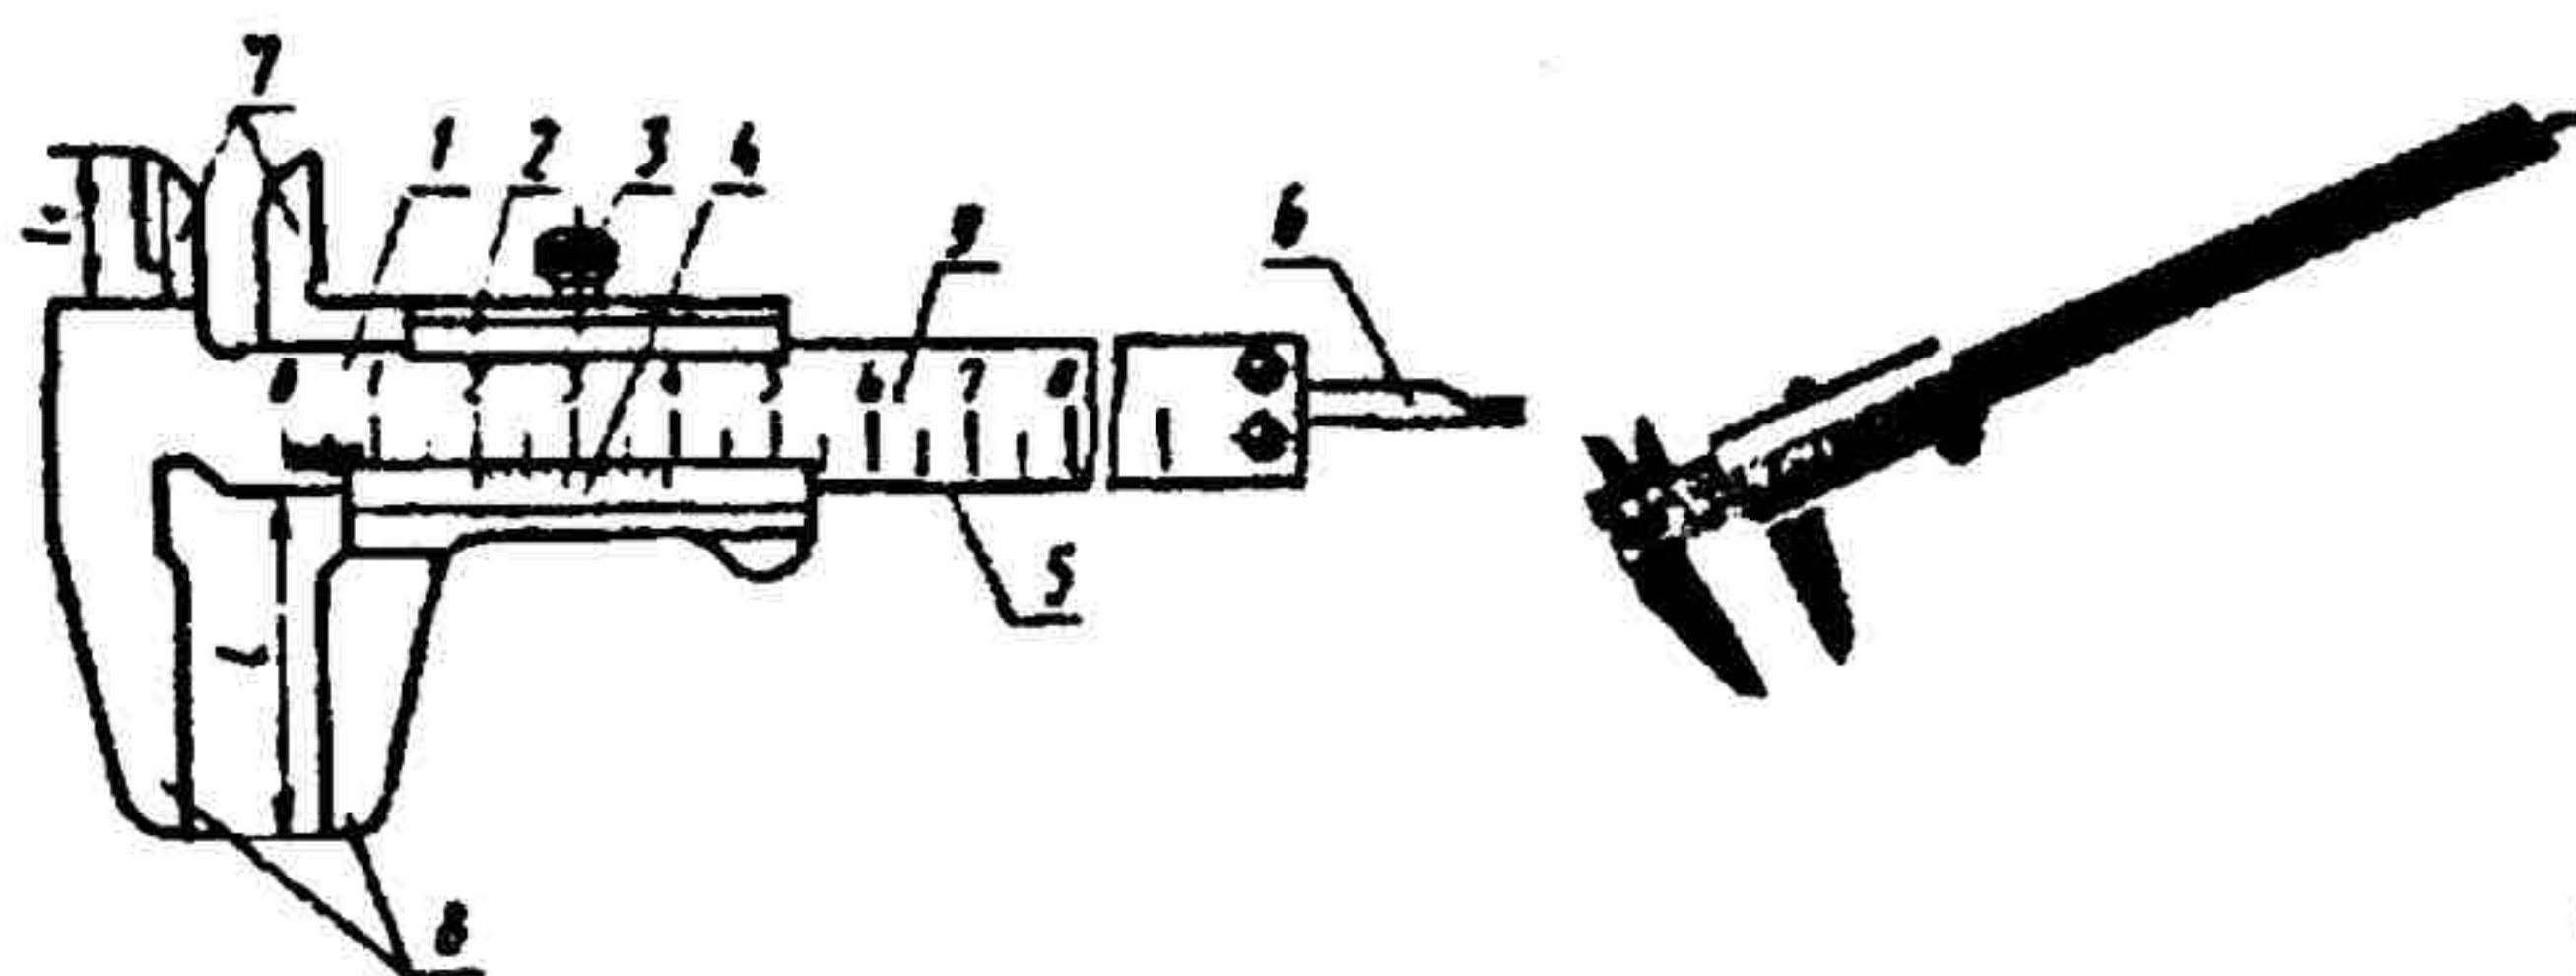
Штангенциркуль с глубиномером ШЦ-1-1250
